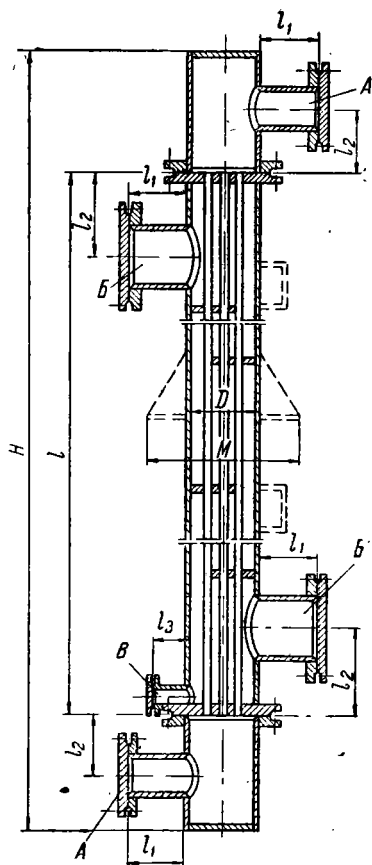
Одноходовой теплообменный аппарат типа ТН с диаметром корпуса 159 или 273 мм, имеющий две камерные сварные крышки с плоскими донushками.
